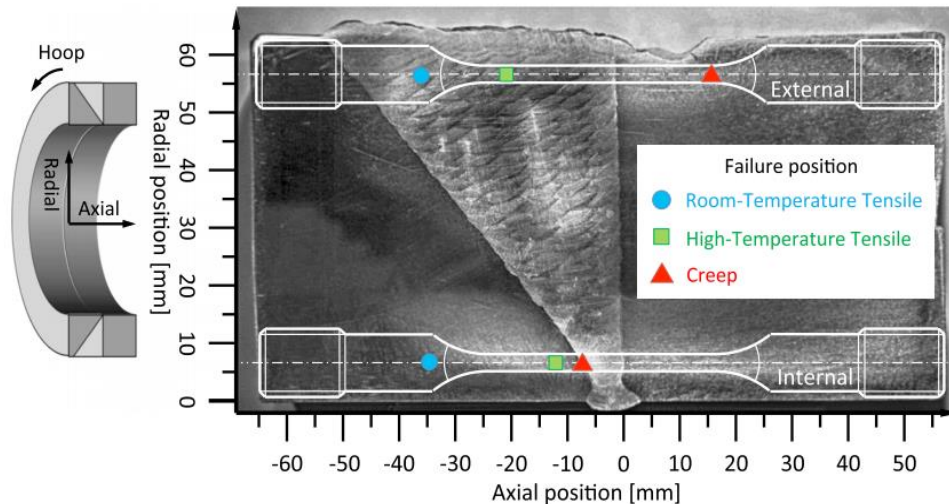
Soudure en acier inoxydable austénitique à section épaisse (64 mm) montrant les emplacements d'extraction des éprouvettes de fluage. Les positions de rupture des éprouvettes dans les essais de traction par soudure croisée et les essais de fluage sont également indiqués (notez que les éprouvettes à température ambiante utilisaient une longueur de jauge plus longue de 70 mm). Le schéma montre l'orientation de la soudure dans la section du tuyau [22].
